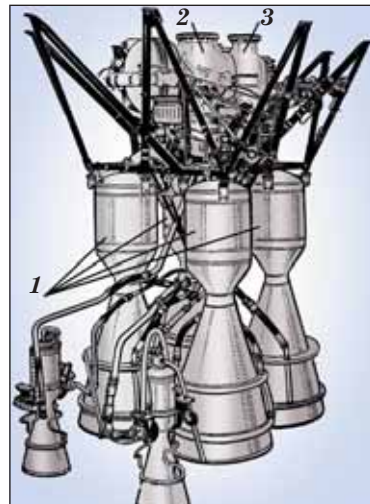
Ракетный двигатель корабля «Восток». Сила тяги двигателя 1 МН
